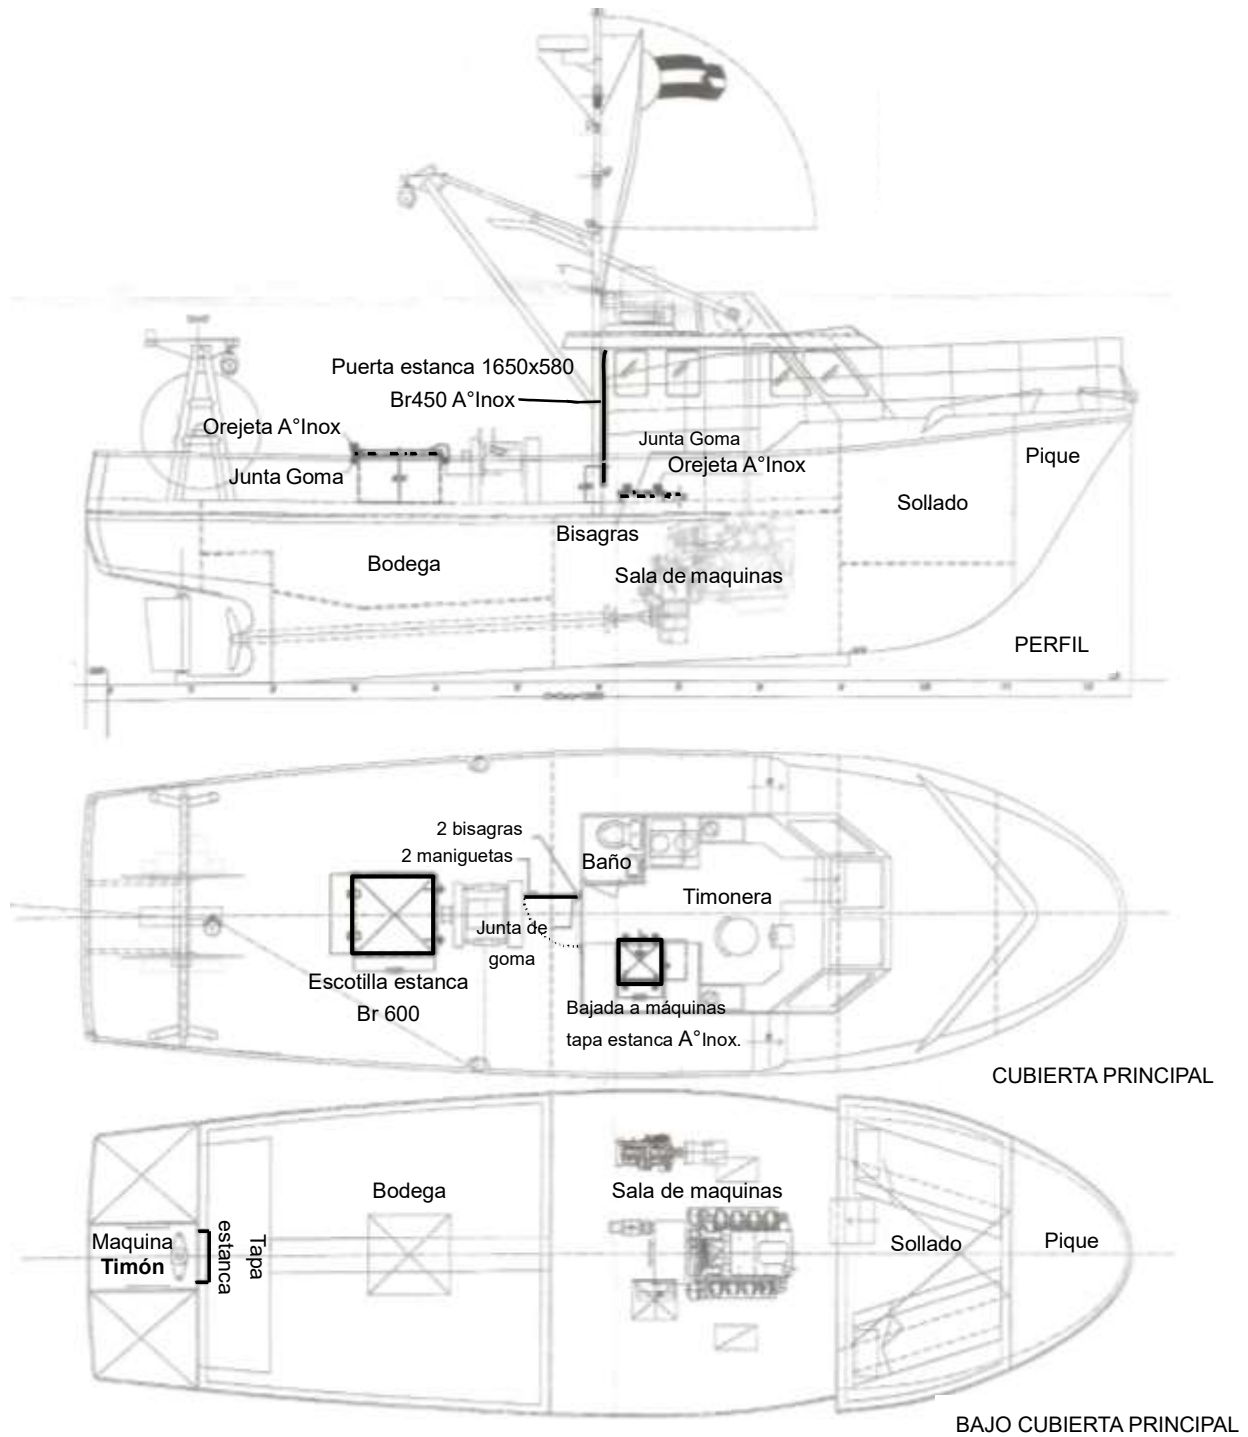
Plano de cierres estancos del B/P Innovator, vista de perfil, de la cubierta principal y bajo cubierta principal
